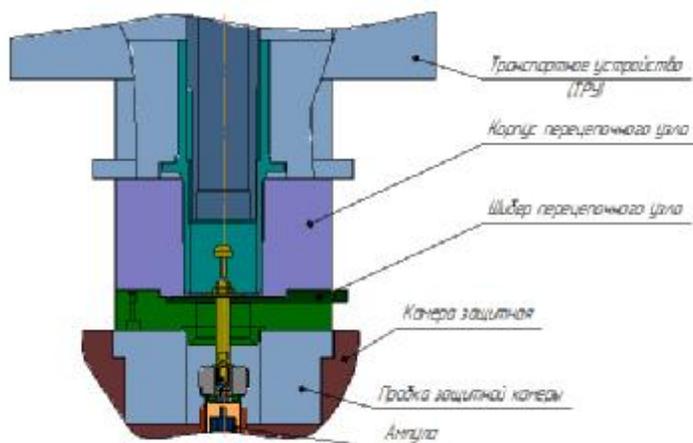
Перецепочный узел для стыковки ТрУ с пробкой защитной камеры
